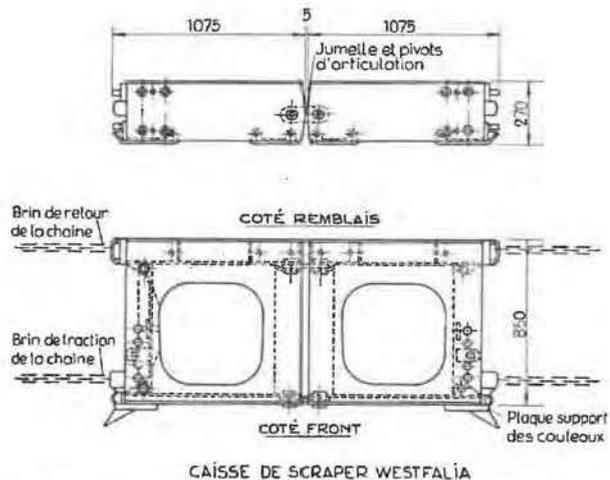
Caisse de scraper à deux éléments, le brin de retour de la chaîne passe dans un tube guide situé sur la paroi arrière de la caisse.
